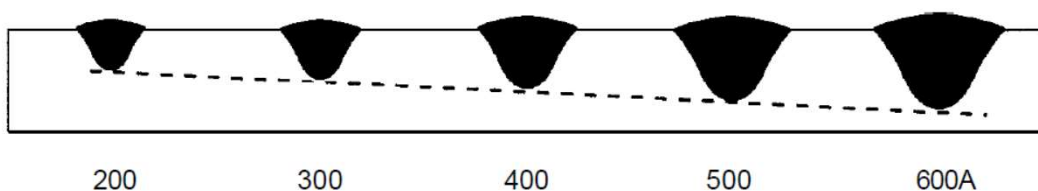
Efecto del amperaje en la geometría del cordón de soldadura (8).
